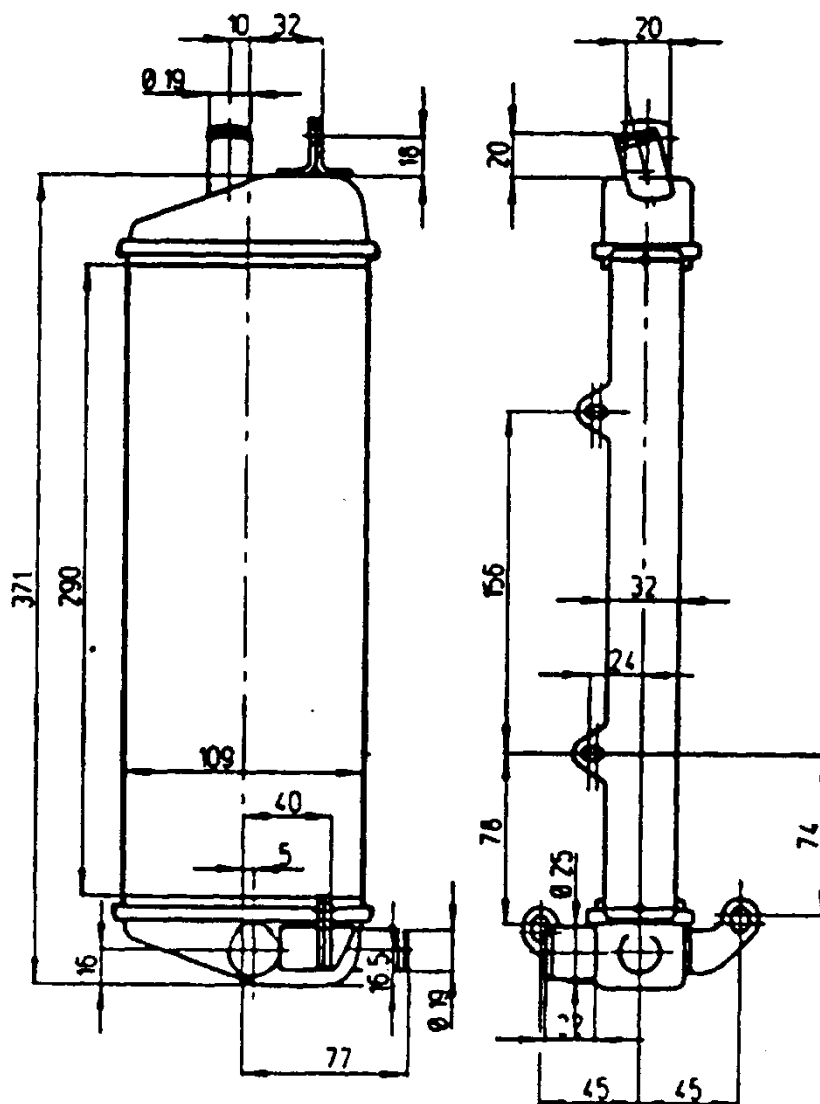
а. Двухсекционный высокий радиатор для двигателя, установленного свечами вниз
